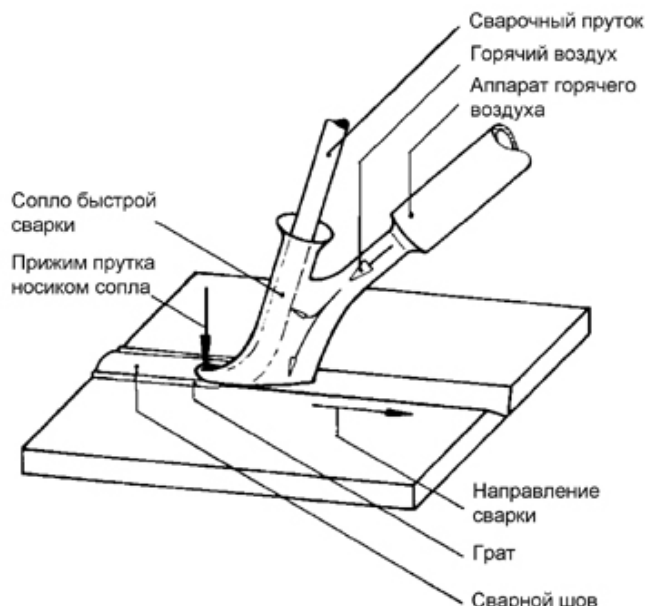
Выполнение сварки соплом быстрой сварки
